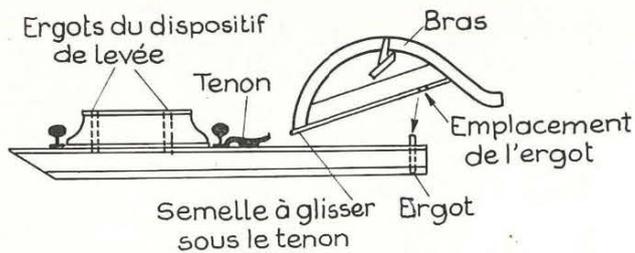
Allonge, avec points de fixation du dispositif de levée et de la rampe.
